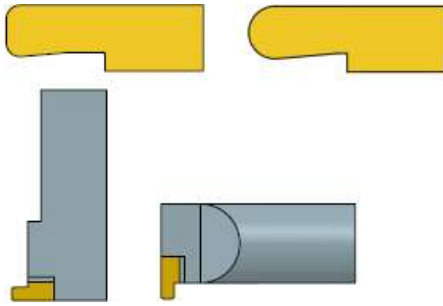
Types Corps d'outil - Plaquette de Tournage
